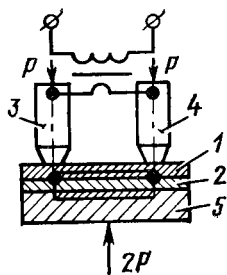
Схема односторонней точечной сварки:
